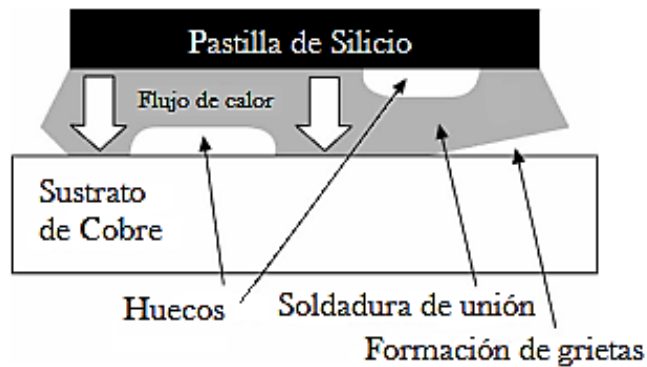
Roturas y formación de huecos en la soldadura de unión [27].
